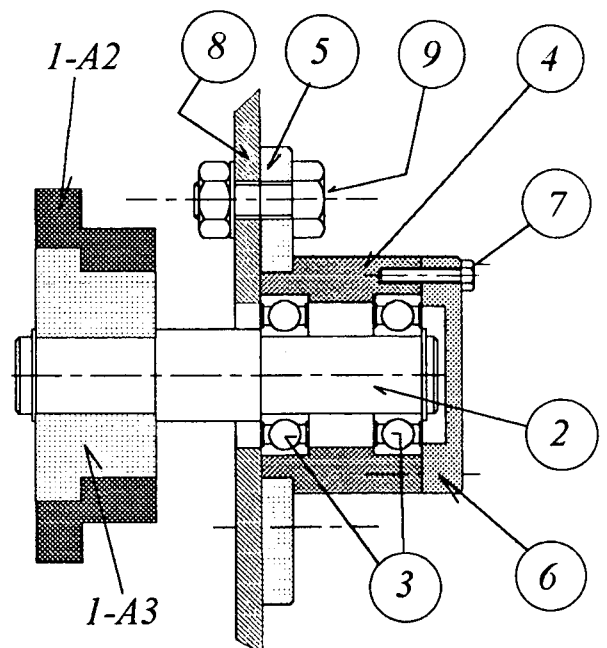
Mancal com tampa e roda dentada 16 dentes- A-2
